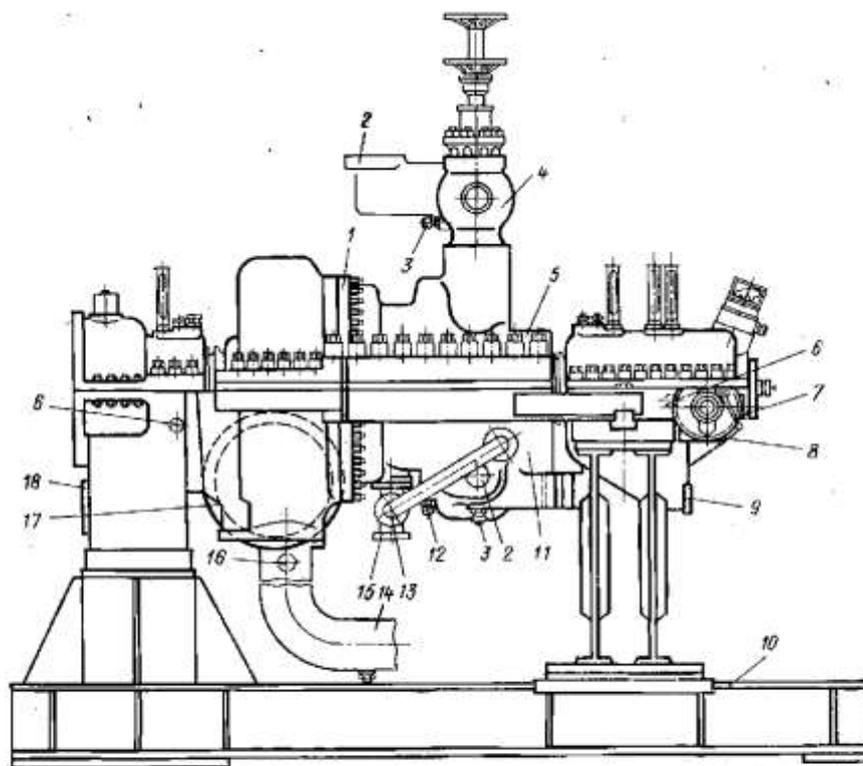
Общий вид корпуса ТВД ГТЗА:
